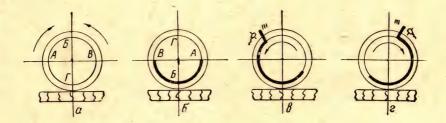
Последовательность работ при сварке поворотных стыков.
